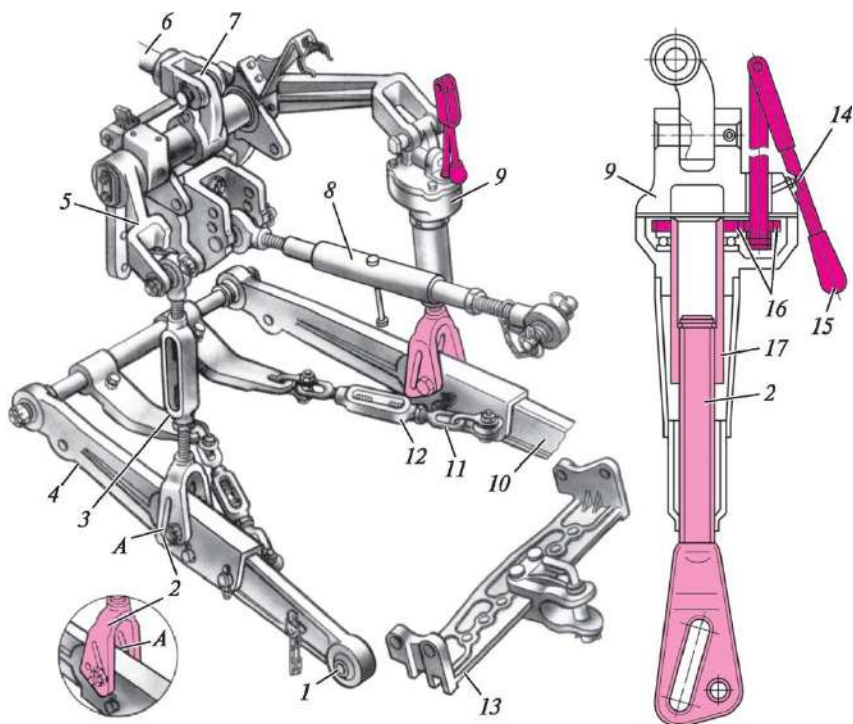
Трехточечная схема механизма навески трактора МТЗ-80: 1 — устройство; 2 — регулируемый раскос; 3 — сферический (шаровой) шарнир; 4 — вилка раскоса; 5 — левый раскос; 6, 7 — передняя и задняя части продольной тяги; 8, 9 — подъемный и поворотный рычаги; 10 — шток гидроцилиндра; 11 — центральная тяга; 12 — редуктор правого раскоса; 13 — ограничительная цепь; 14 — стяжка цепи; 15 — прицепное устройство; 16 — пресс-масленка; 17 — рукоятка; 18 — шестерни; 19 — труба раскоса; 20 — прорезь
